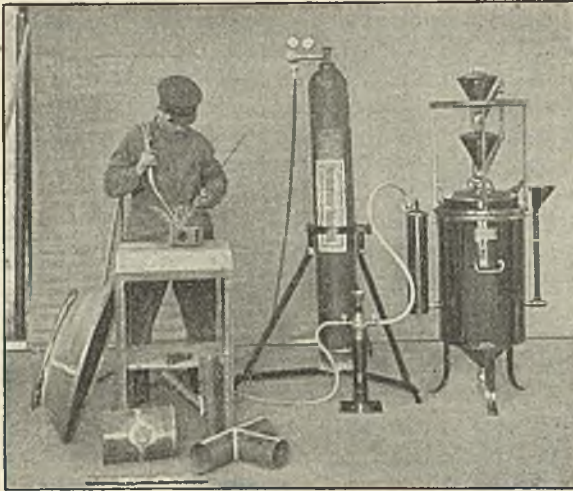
Azetylen-Schweißapparat in Betrieb.
